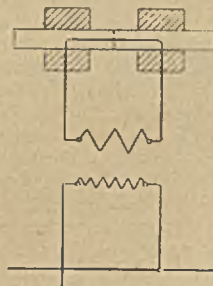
Widerstandsschweißung mittels transformierten Wechselstromes: Stumpfschweißung.
